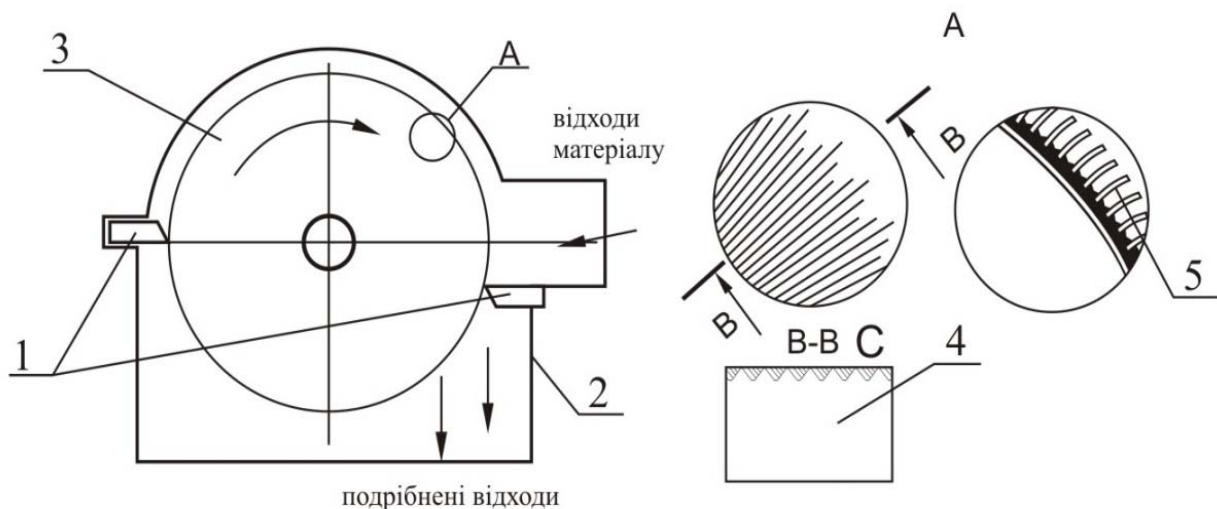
Голкофрезовий подрібнювач: а) дезінтегратор; б) пластинчатий ротор; в) голчатий ротор; 1 - ножі статора; 2 - корпус; 3 - ротор; 4 - пластини дисмембратора; 5 - голки голкофрези
